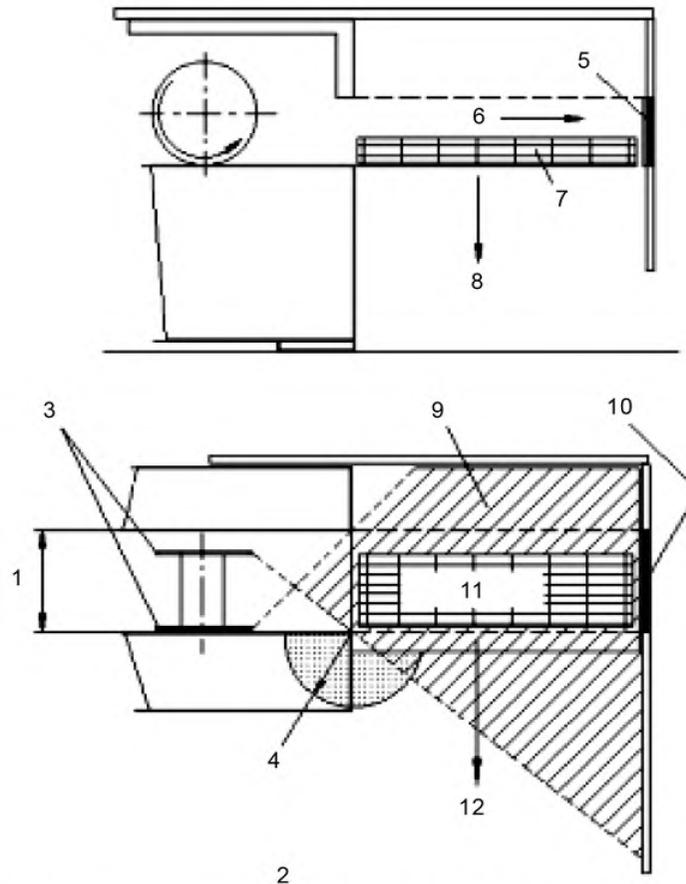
Туннель для отвода (и снятия обрабатываемой заготовки)
